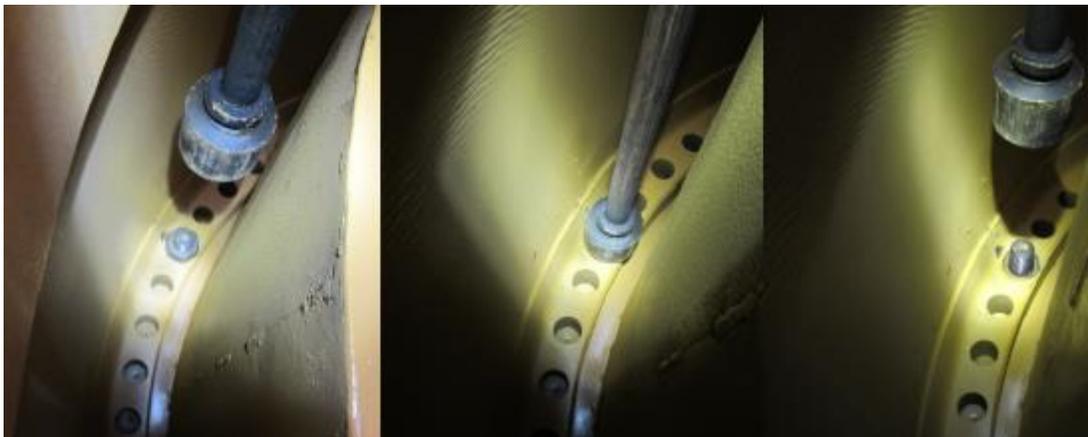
Imagen de la cámara del sistema extractor de tuercas.
